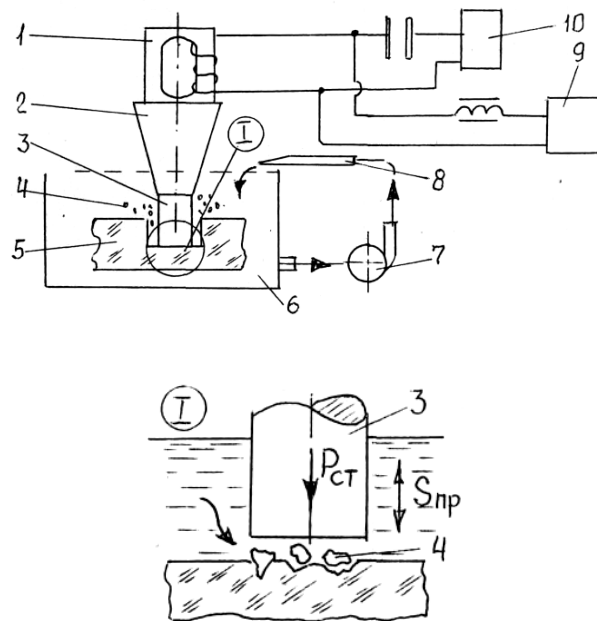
Схема прошивання отворів: 1 – УЗ-перетворювач; 2 – концентратор; 3 – інструмент-пуансон; 4 – суспензія абразивна; 5 – заготовка; 6 – ванна; 7 – помпа; 8 – патрубок; 9 – джерело струму; 10 – генератор УЗ частоти
